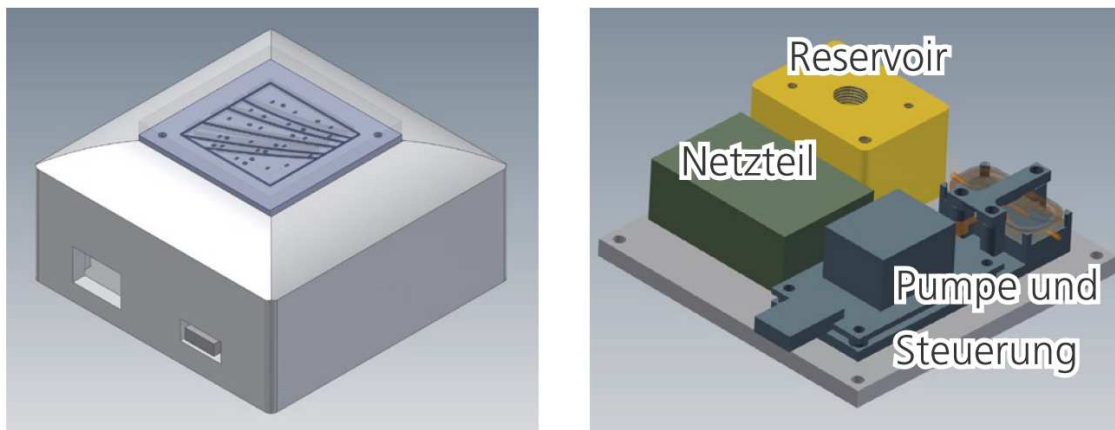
Demonstratorgehäuse und Gehäusegrundplatte
